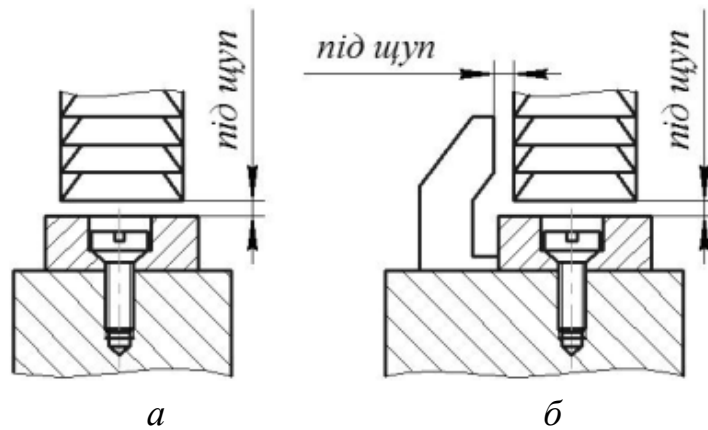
Типи установ: а - висотний; б - кутовий
